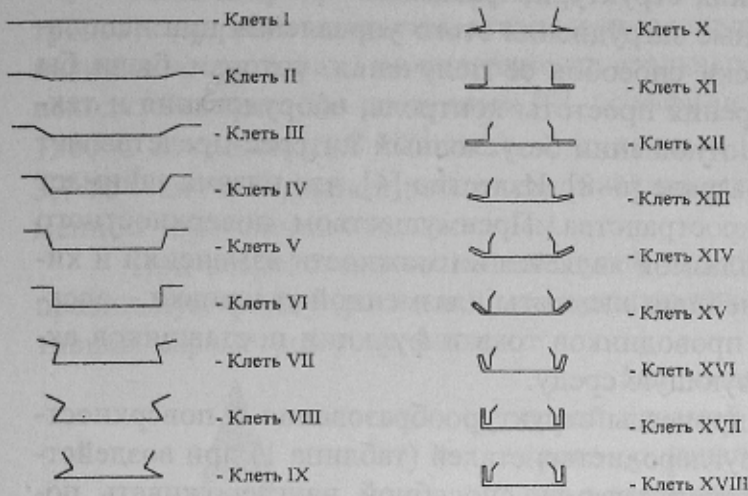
Профилировка планки в сдвоенном виде из одной заготовки
